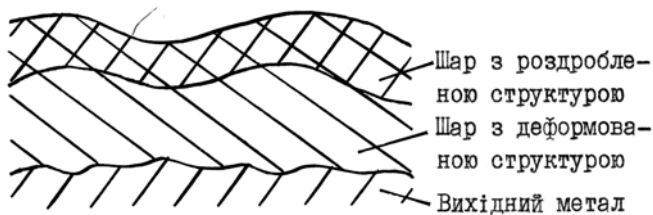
Будова поверхневого шару після механічного оброблення вуглецевої сталі
